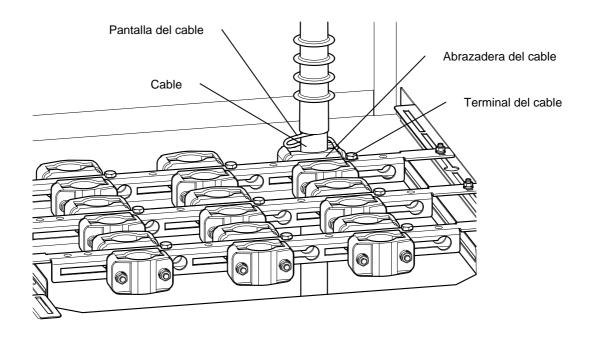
AMC9: Conexión de cables para 4, 5 y 6 cables de salida
